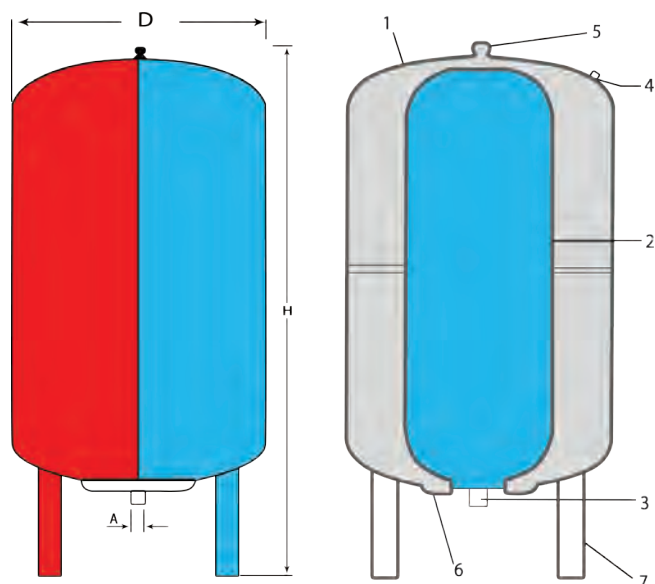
Устройство и габаритные размеры гидропневматических баков
